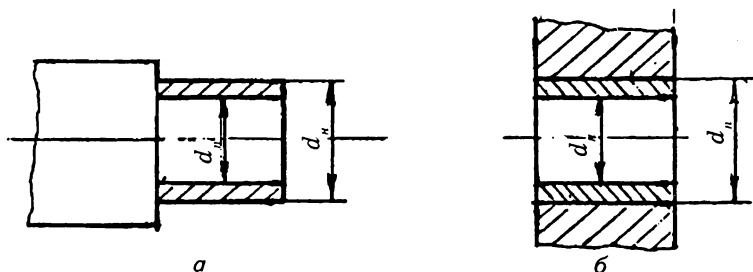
Установка дополнительной детали на вал (а) и в отверстие (б):
